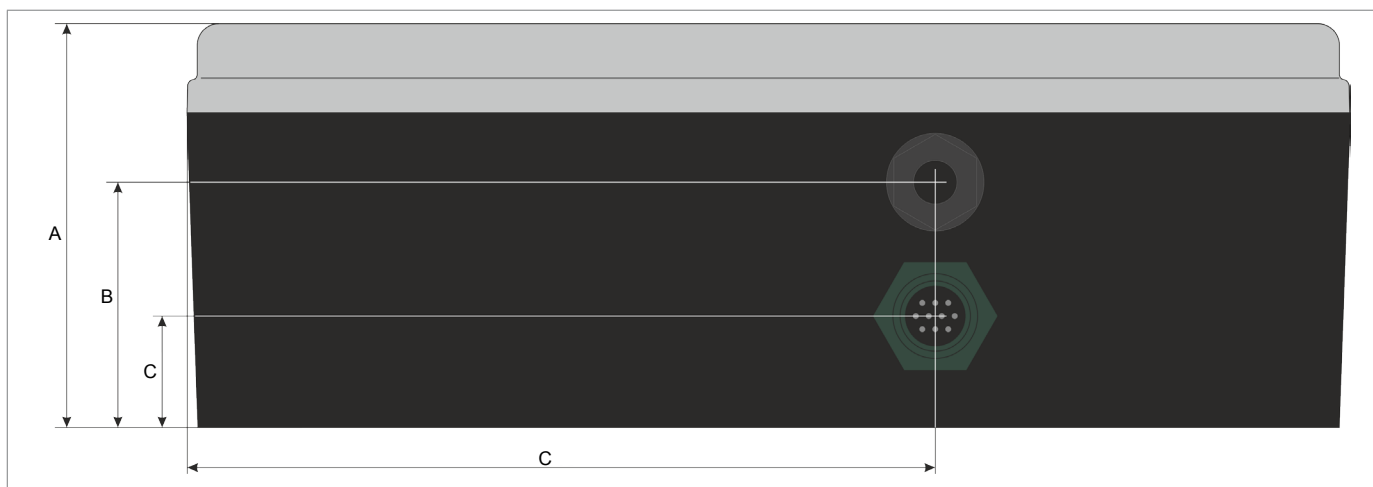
Vista esterna lato superiore versione connettore MIL
